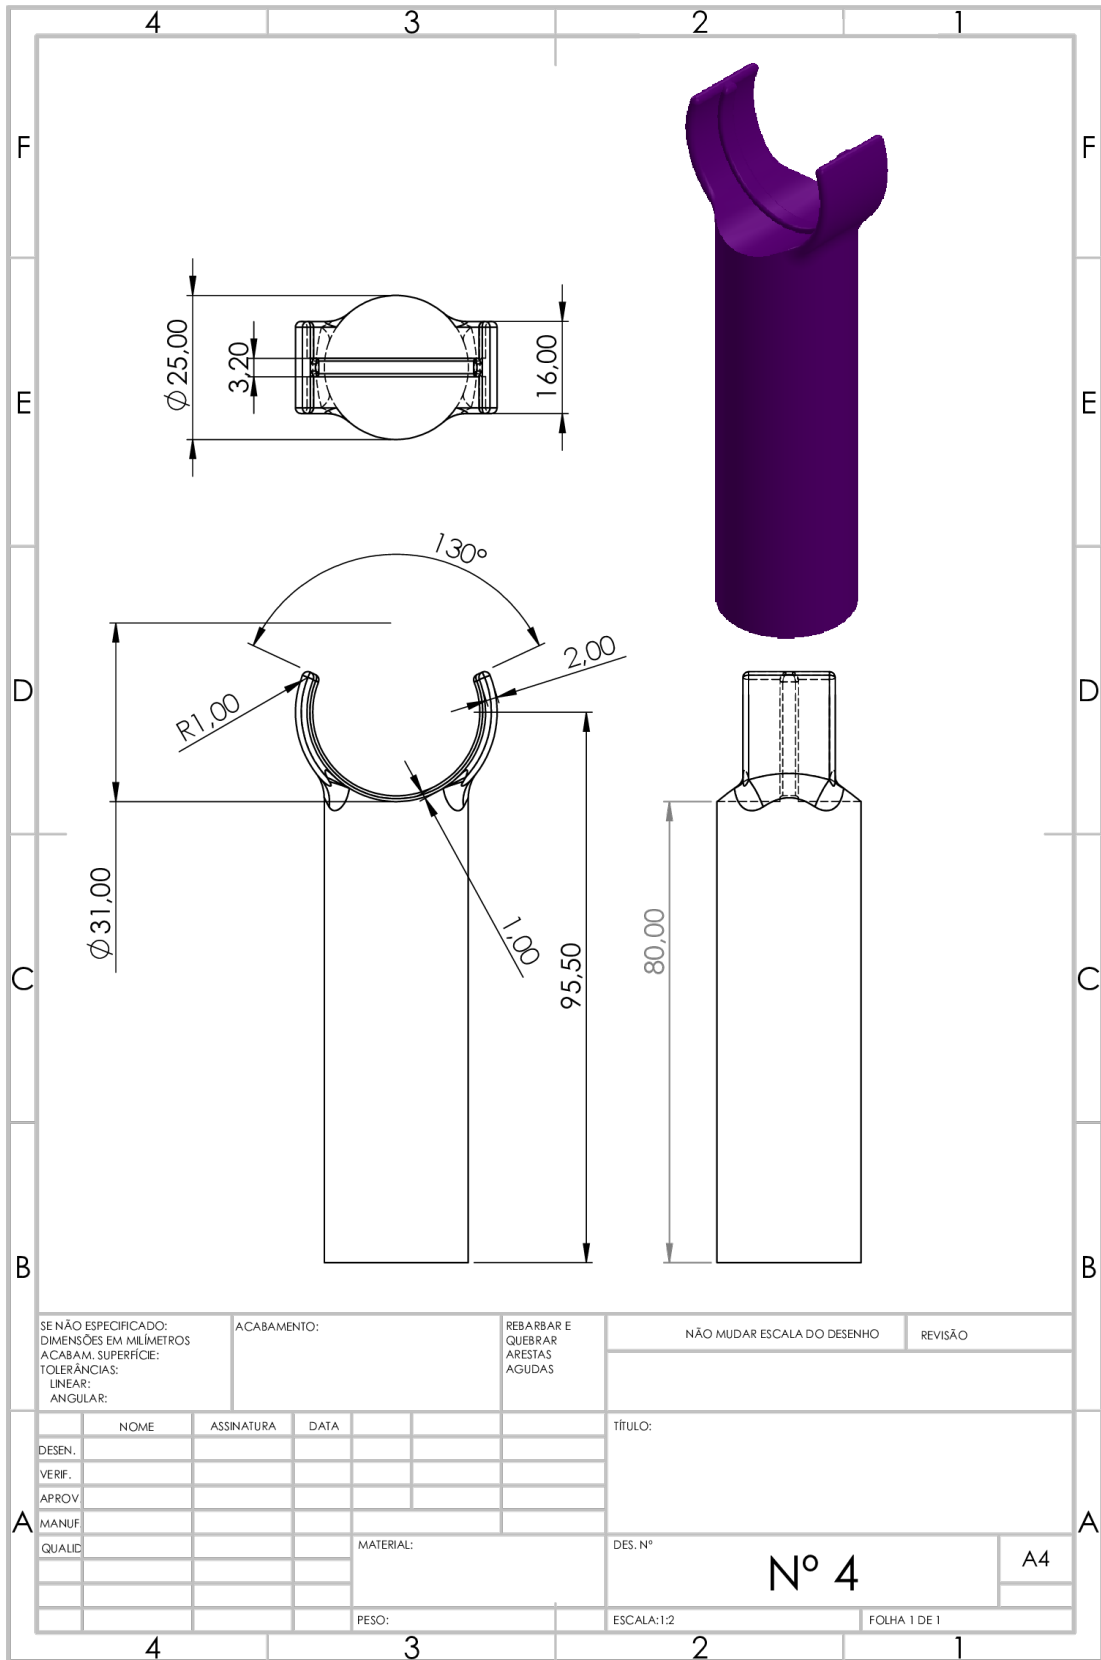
Desenho Técnico do Suporte do Microscópio
